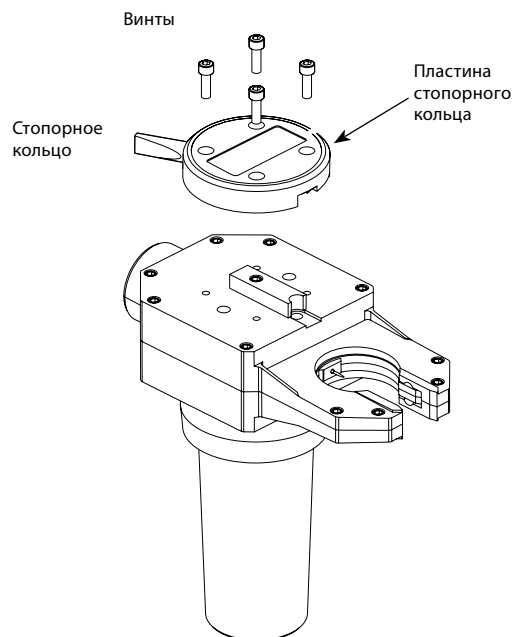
Снятие стопорного кольца и пластины стопорного кольца
